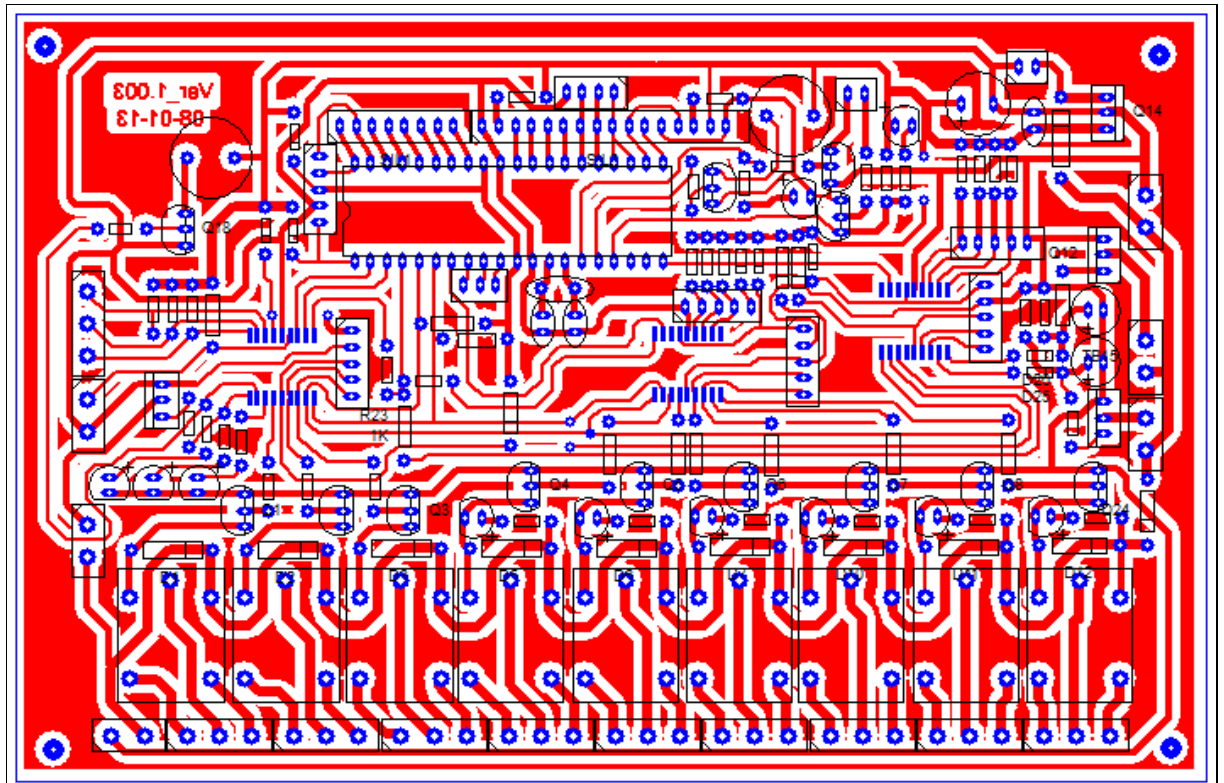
Circuito PCB para el Sistema de Control mediante SMS
